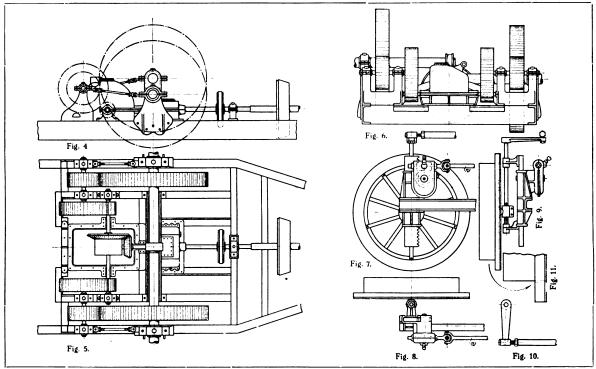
bis 6. Getriebe des Stock-Motorpfluges. Maßstab 1:31,5.
